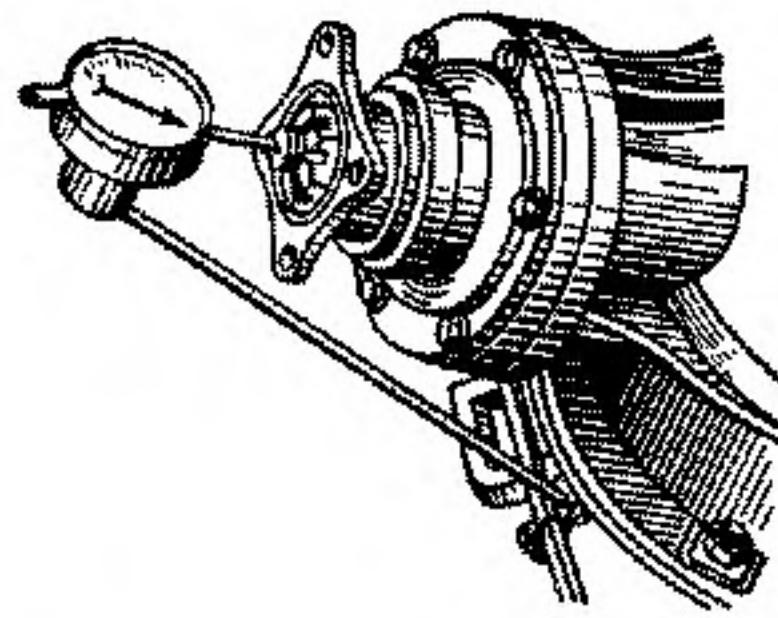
Определение осевого люфта в подшипниках вала ведущей шестерни главной передачи индикатором
